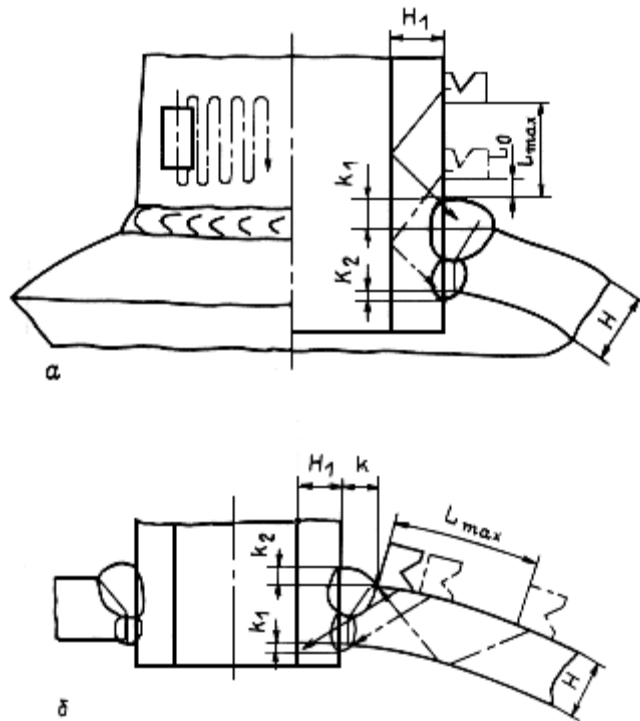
Схема контроля углового сварного соединения: а - по наружной поверхности патрубка; б - по наружной поверхности корпуса
